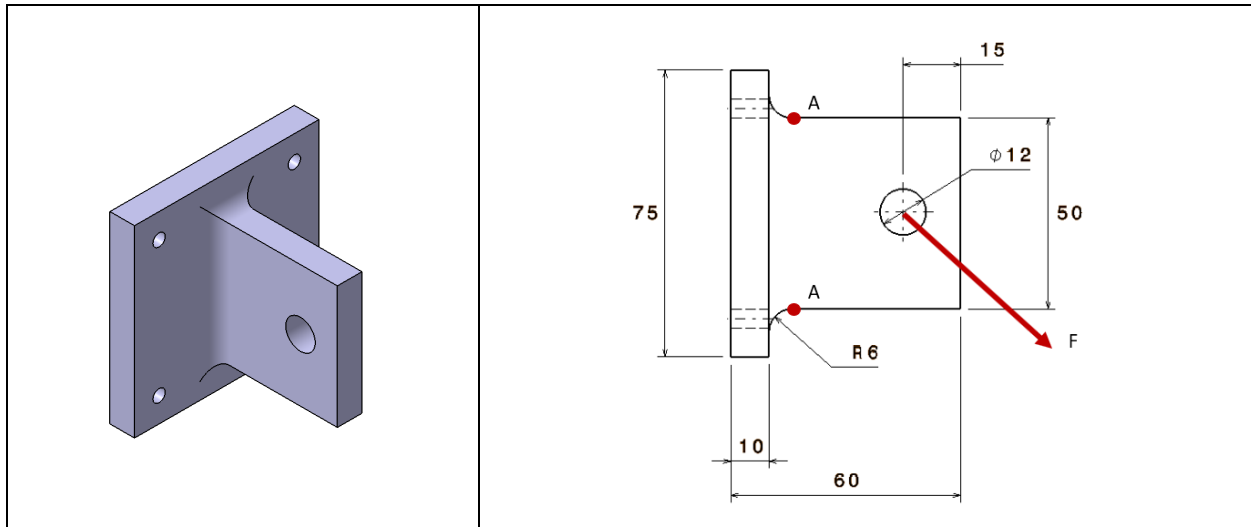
Pièce mécanique sous chargement statique (dimensions en mm). À gauche : vue isométrique; à droite : dessin technique.
